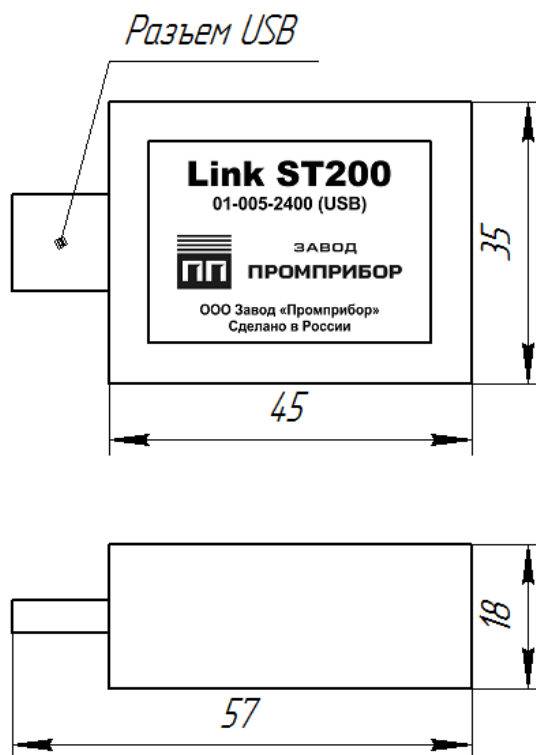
Внешний вид и размеры модема в исполнениях ST200-01-005-0433 (USB) и ST200-01-005-2400 (USB)
